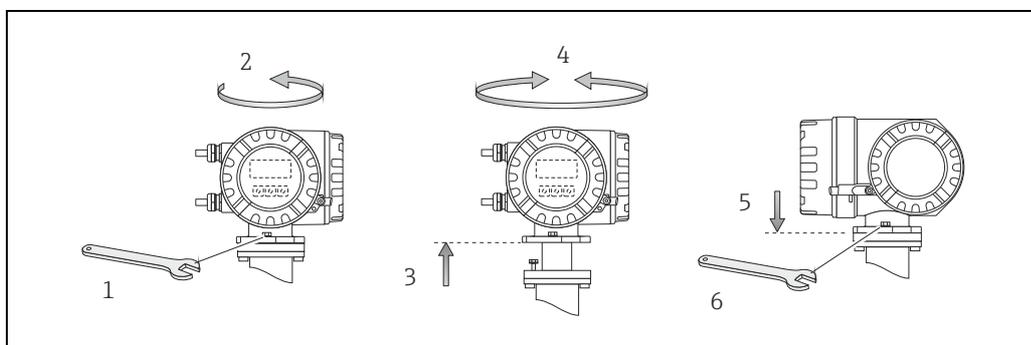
Rotación de la caja del transmisor (caja de aluminio para montaje en campo)
